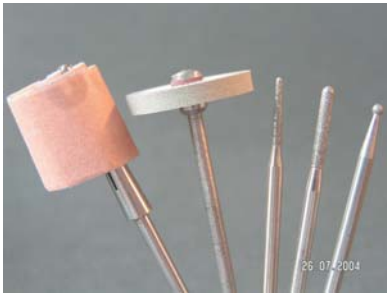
Zum Bearbeiten verwende ich Sandpapier, einen weißen Universalpolierer und Diamantschleifer. Instrumente von Komet-Brasseler haben eine gute Standzeit.
